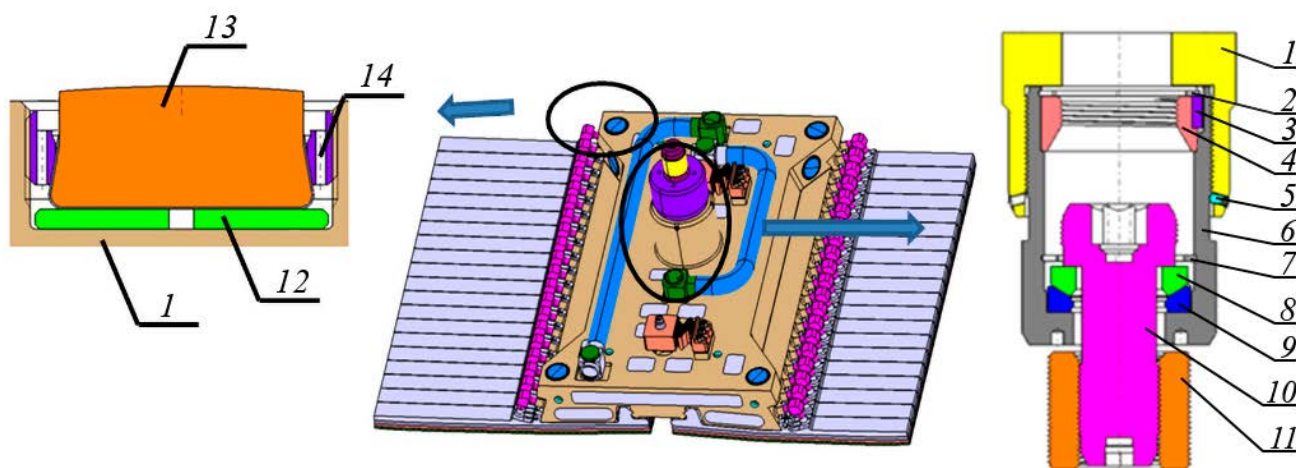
Общий вид СК ППС: 1 — НКПС; 2 — стопорное кольцо; 3 — шпонка; 4 — парковочная втулка; 5 — стопорный винт; 6 — стакан; 7 — стопорное кольцо; 8 — сферическая шайба; 9 — коническая шайба с ЭИП; 10 — болт; 11 — резьбовая втулка ЗБ; 12 — диск; 13 — КЭИН; 14 — фиксирующая гайка
